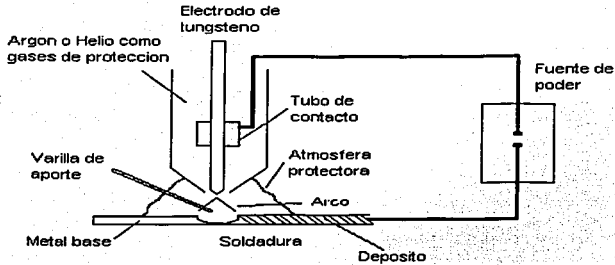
Esquema de los componentes y parámetros en el proceso de soldadura GTAW [3].
